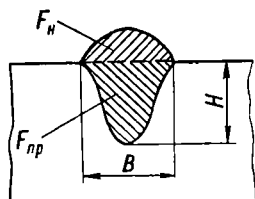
Геометрические параметры сечения сварного шва
